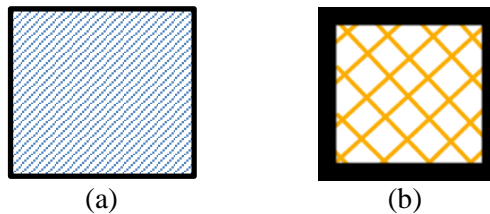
(a) Pièce massive dessinée en BE ; (b) pièce réalisée par la machine BMD
